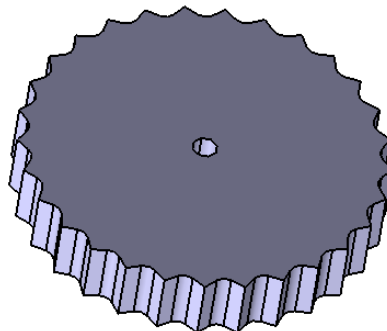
Engranaje: Rueda dentada modelada en CATIA
